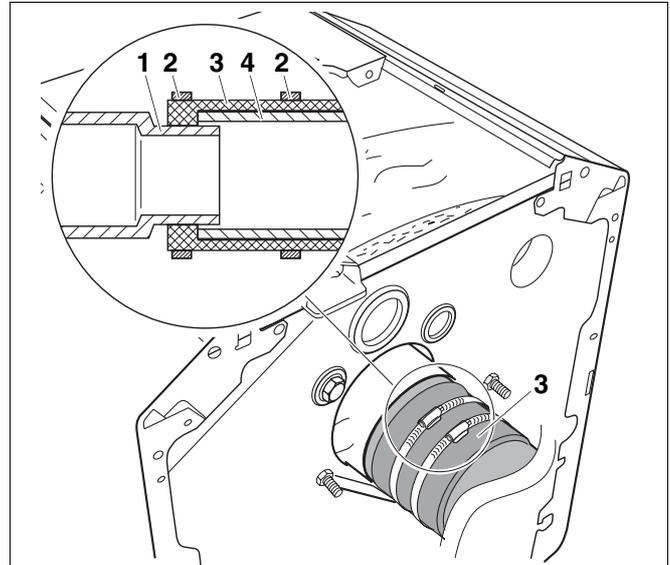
Abgasrohr-Abdichtmanschette (Außenwandanschluss) montieren
